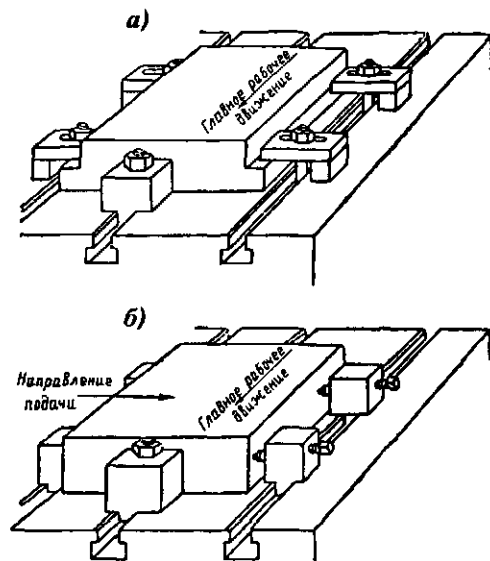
Схемы установки и закрепления деталей с плоскими опорными поверхностями
